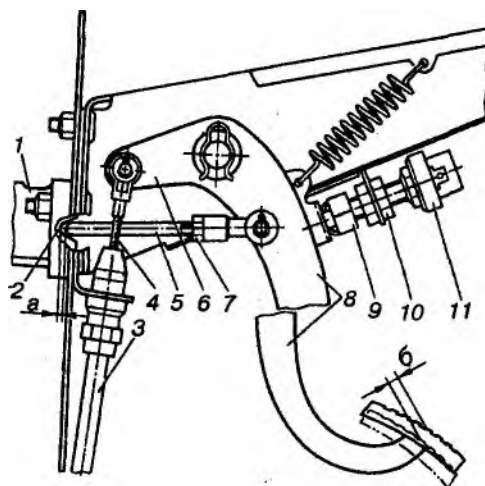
Регулировка свободного хода тормозной педали автомобиля ЗАЗ-1102:
